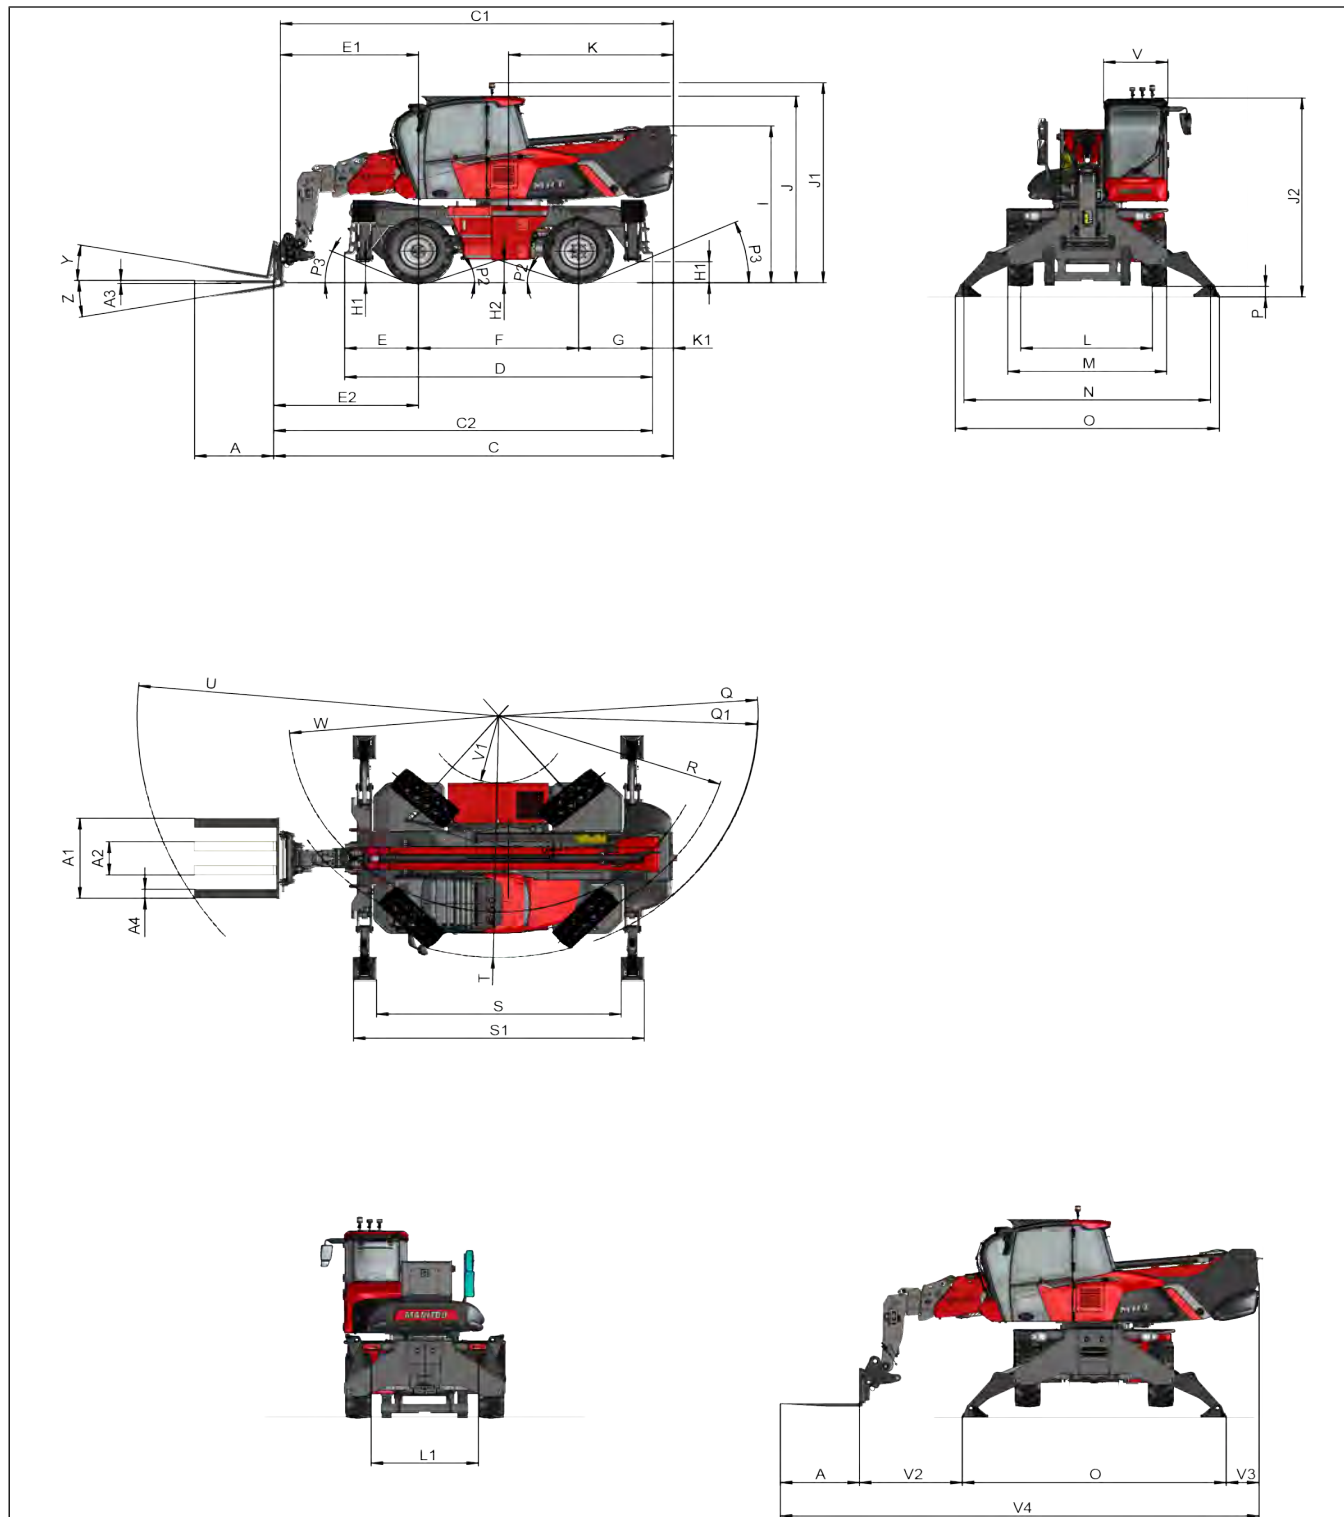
Dimensions (vue latérale, vue de face et vue de dessus)
